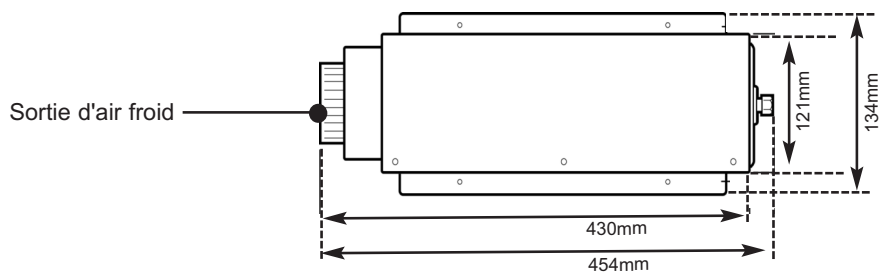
Installation interne - Vue de plan - SH2202 ou SC2202
